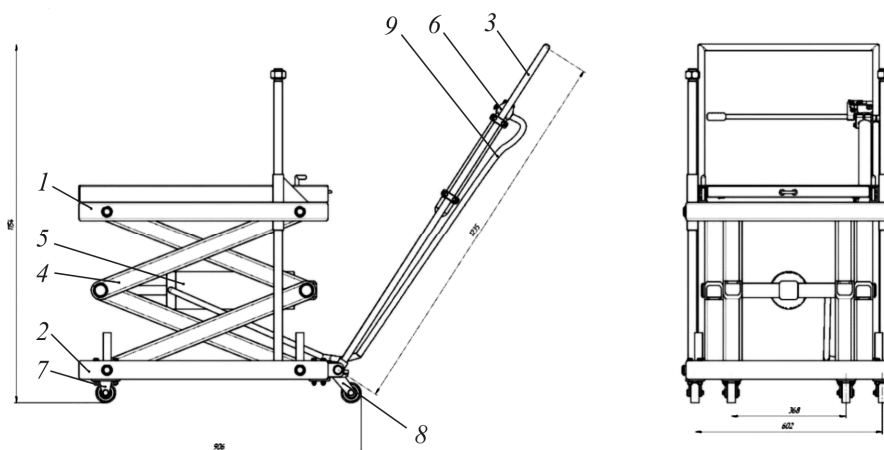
Чертеж общего вида предлагаемой конструкции: 1 – платформа с выдвижной площадкой; 2 – нижняя рама с направляющими; 3 – ручка; 4 – ножничный механизм подъема; 5 – гидроцилиндр; 6 – гидравлический насос; 7 – переднее колесо; 8 – заднее колесо; 9 – шланг высокого давления
